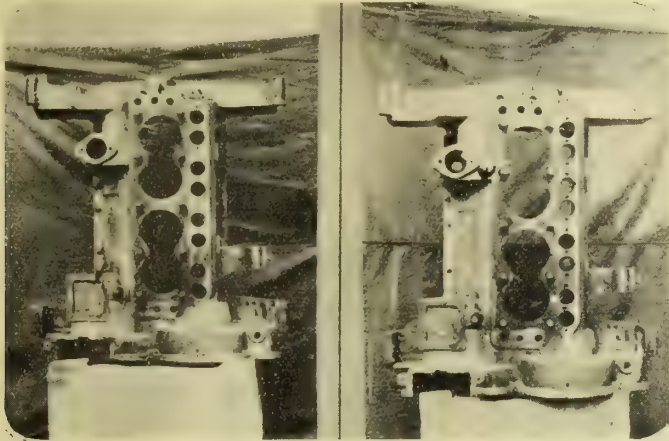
Réparation d'un carter d'automobile en aluminium par soudure autogène.
